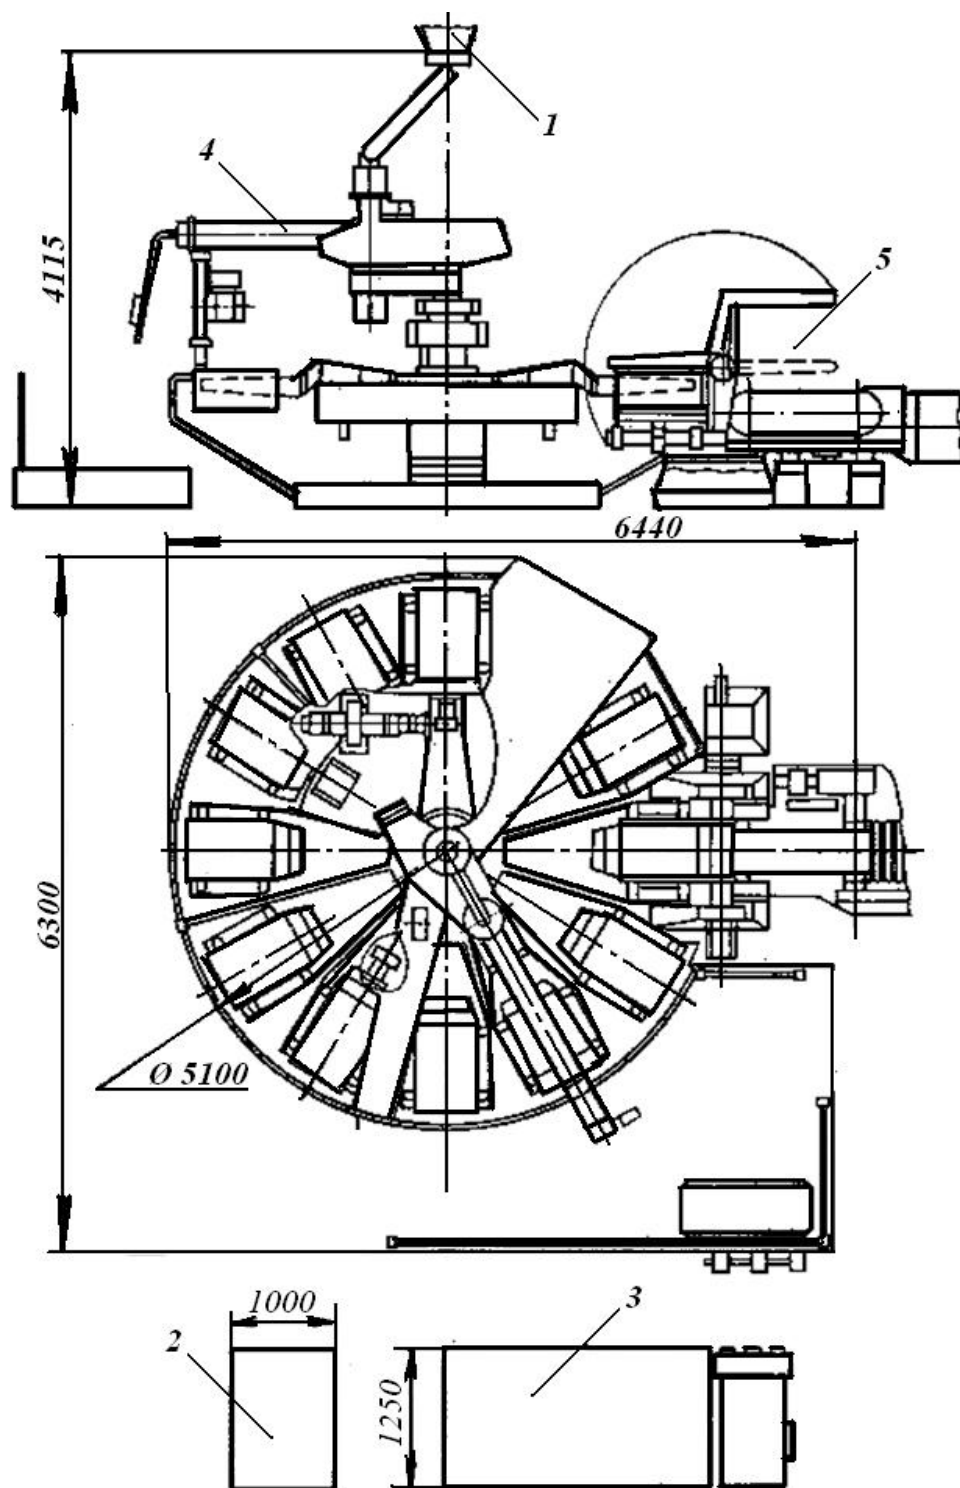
Компоновка 12-позиционной машины для изготовления стержней из холоднотвердеющих смесей:
